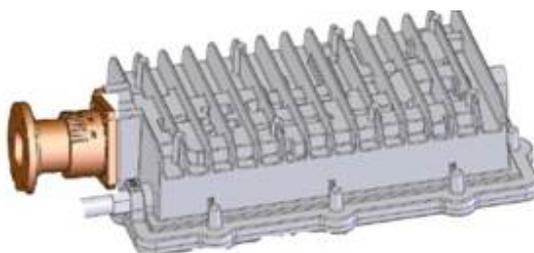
Общий вид приёмопередатчика ODU-2W-KU-P
